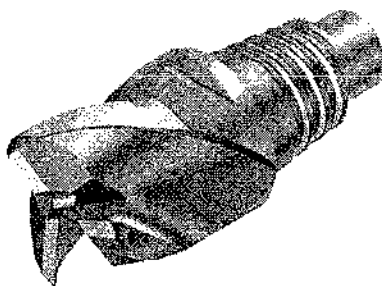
Фреза 316-25SM345-25040A H10F
